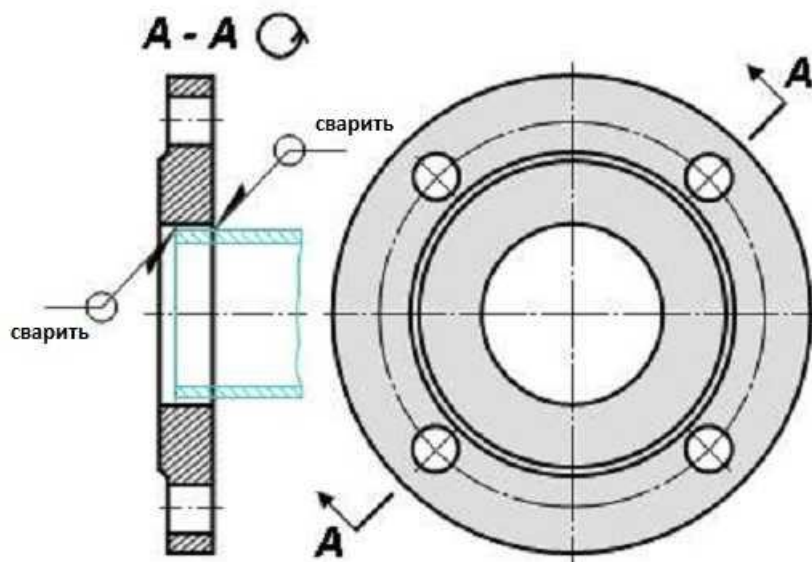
Сварка плоского накладного фланца
